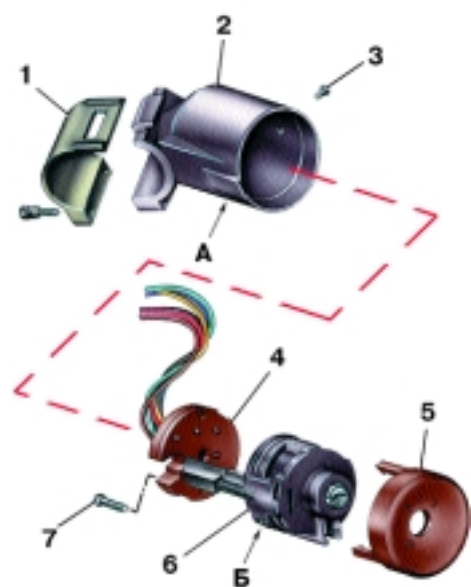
Детали выключателя зажигания KZ813: 1 – скоба; 2 – корпус; 3, 7 – винты; 4 – контактная часть; 5 – облицовка; 6 – замок; А – отверстие для фиксирующего штифта; Б – фиксирующий штифт
